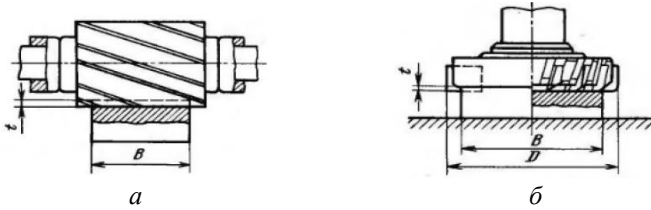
Обработка плоскостей цилиндрическими (*а*) и торцовыми (*б*) фрезами
